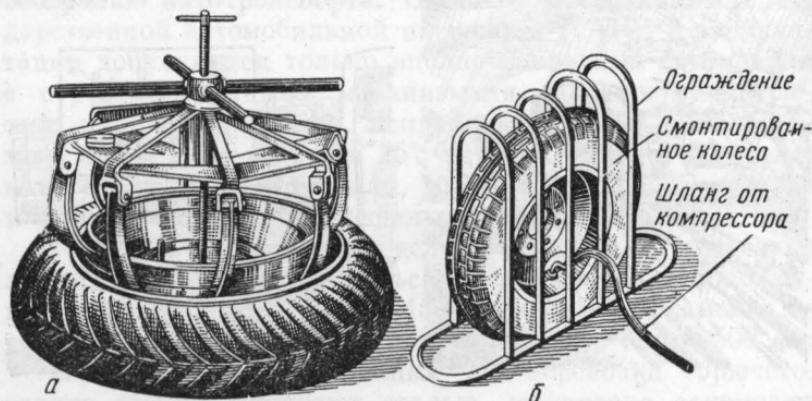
Приспособление для безопасного демонтажа и подкачки шин:
